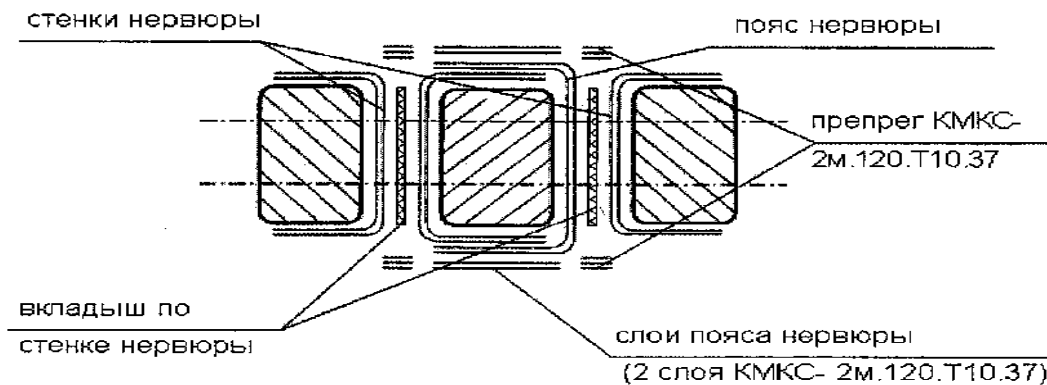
Схема выкладки элементов двустенных нервюр для подформовки
